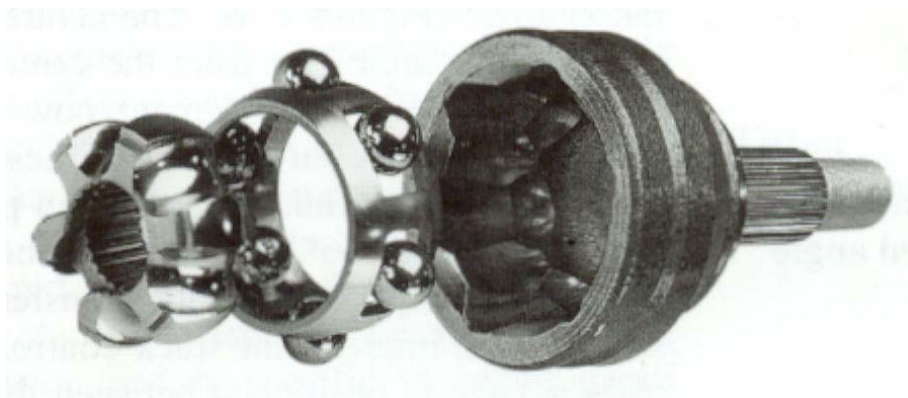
Junta fixa tipo Rzeppa em vista explodida.
